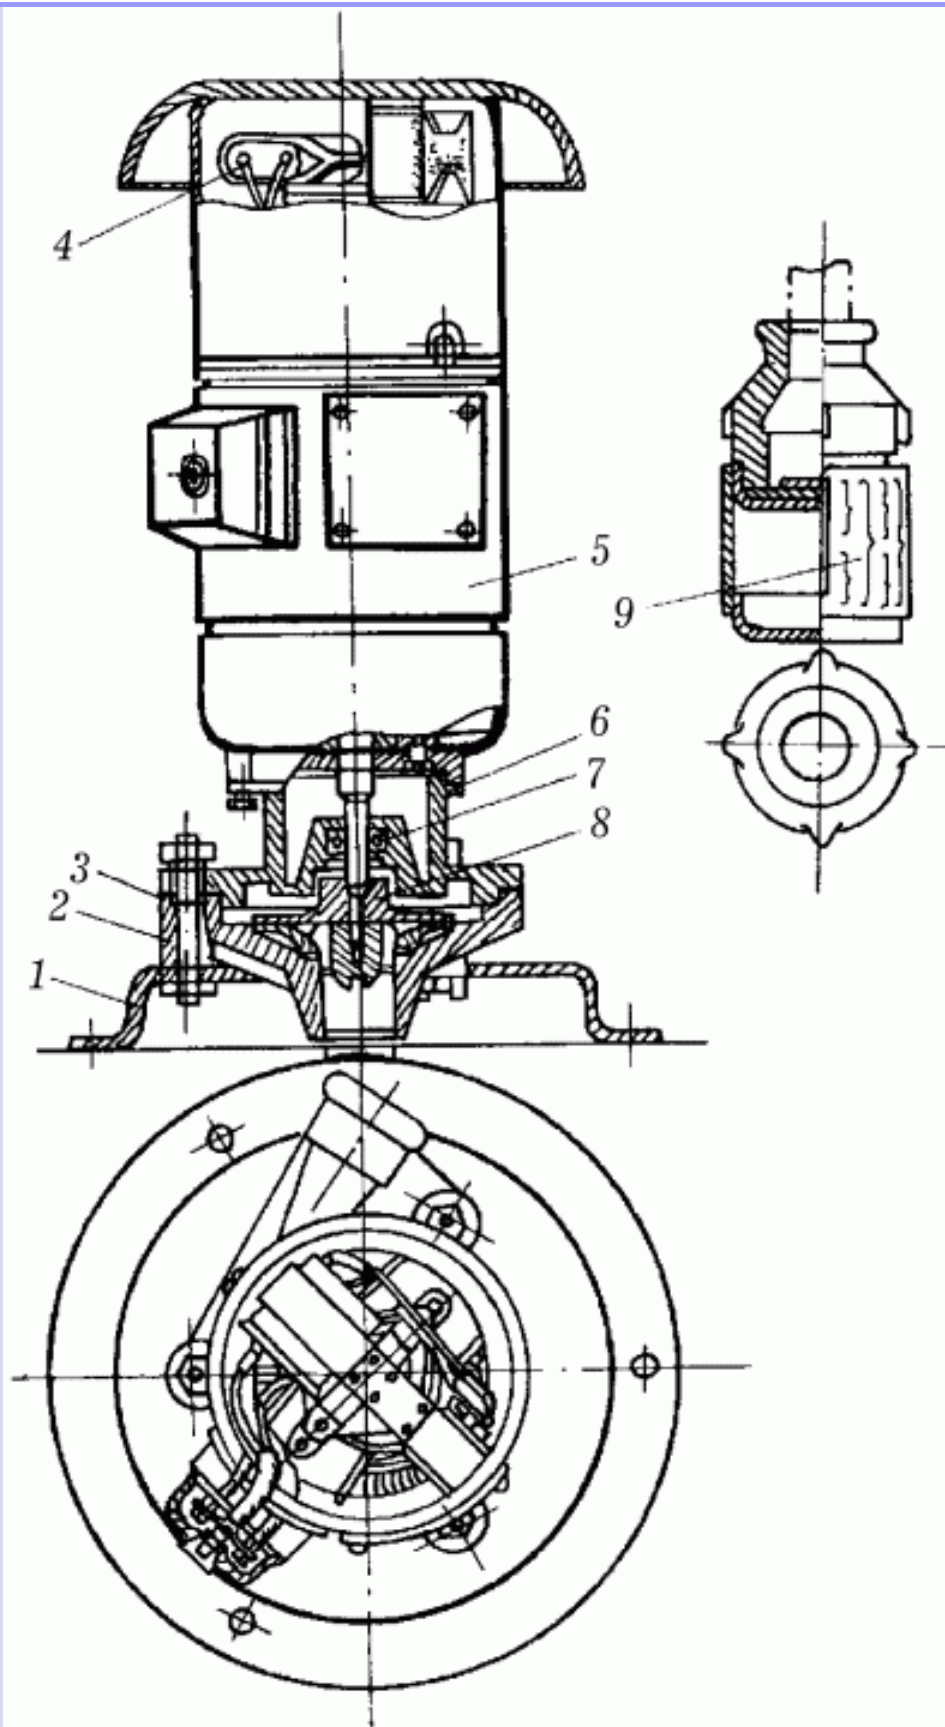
Электронасос центробежного типа «Кама»: 1 – подставка; 2 – основание корпуса; 3 – прокладка; 4 – помехоподавляющее устройство; 5 – электродвигатель; 6 – крышка насоса; 7 – сальник; 8 – рабочее колесо; 9 – приемное устройство.
